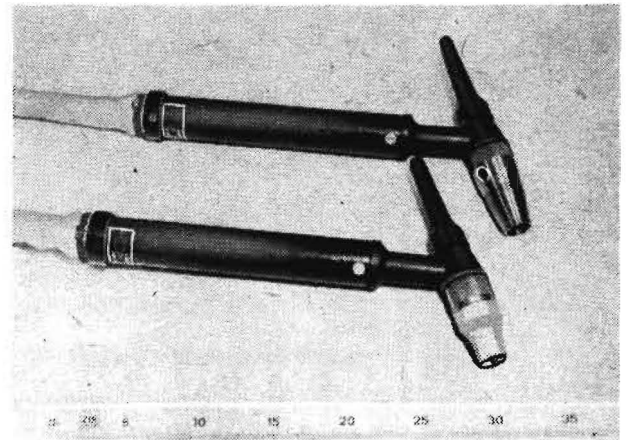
WIG-Schweißbrenner ZIS 290 und ZIS 224
